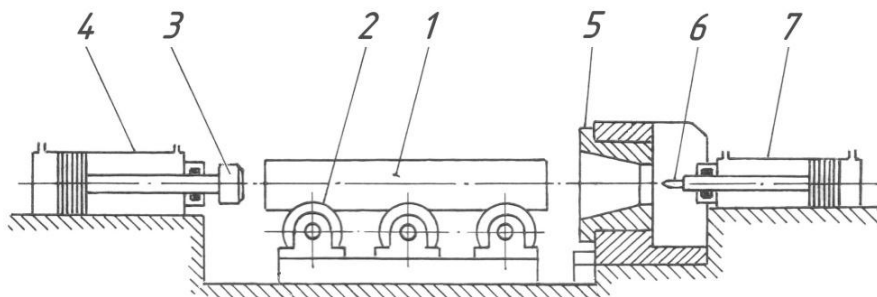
Загальний вид установки: 1 — злиток; 2 — трьохролковий поворотний рольганг; 3 — головка штоку; 4, 7 — гідроциліндри; 5 — матриця; 6 — конічно-циліндричний пуансон
